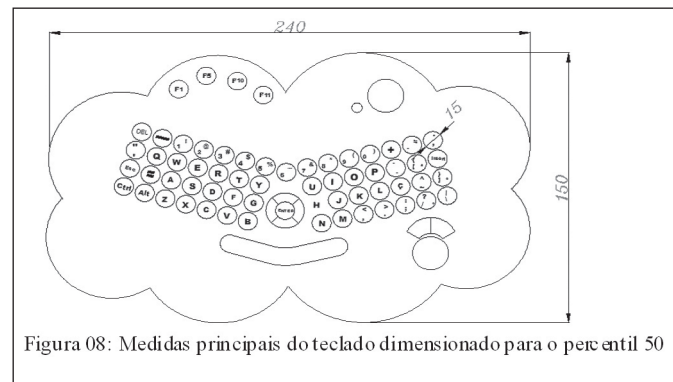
Medidas principais do teclado dimensionado para o percentil 50
